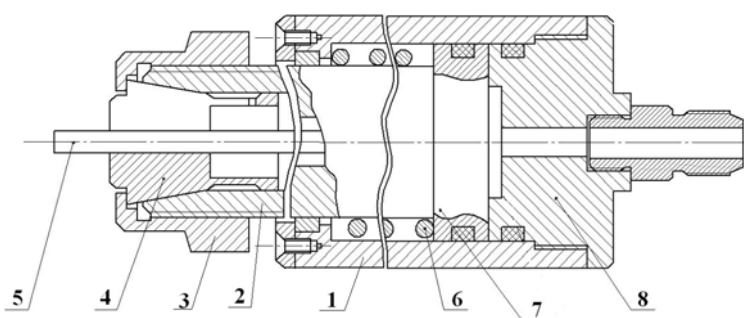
Приспособление для фрикционного нанесения покрытий.
